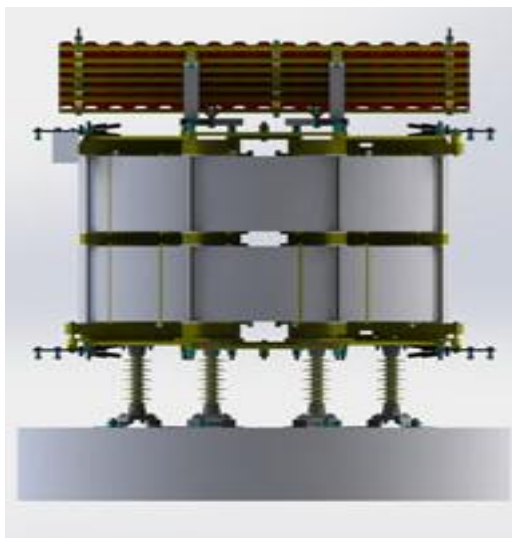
Загальний вид сухого струмообмежувального реактора
